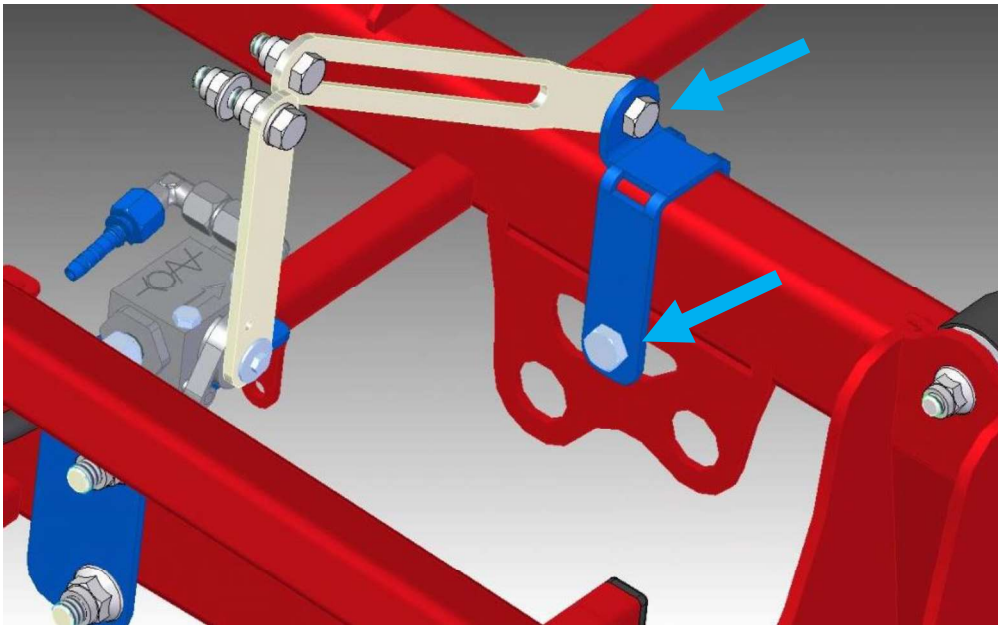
Montage des Befestigungsbleches und Steuergestänges am Seitenrahmen
